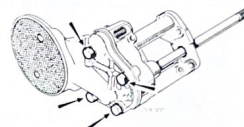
Bomba de aceite de un motor tipo 813. Las flechas indican los tornillos de unión de la tapa al cuerpo de la bomba.
